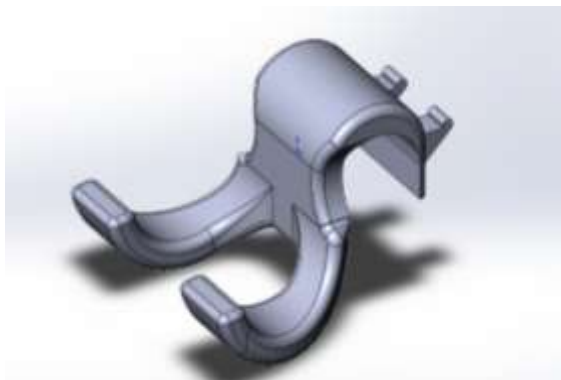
Держатель излучателя аппарата лазерной эпиляции
